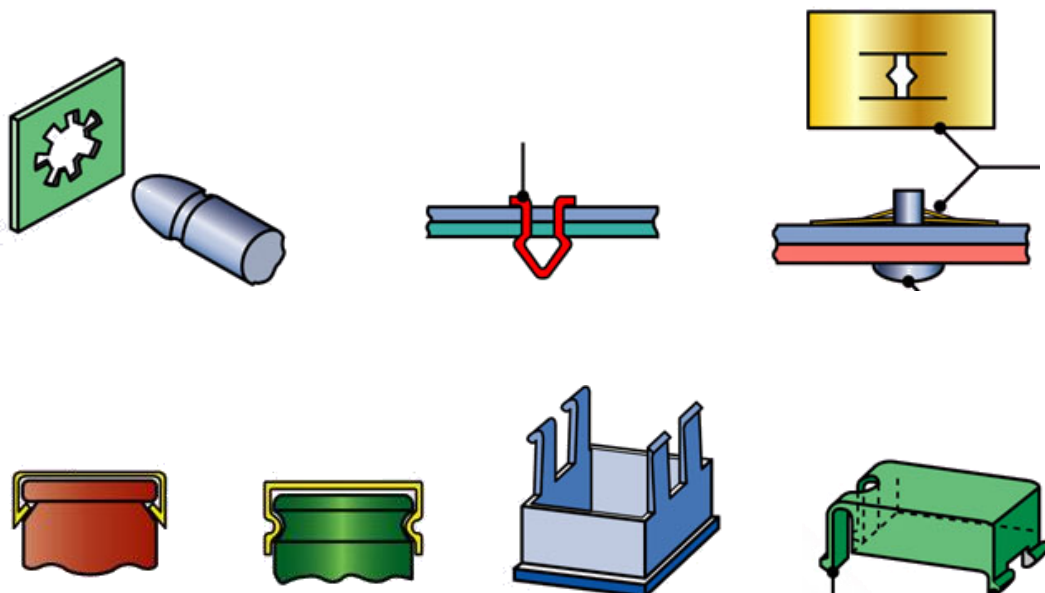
Конструктивні різновиди з'єднання з пружними деталями
